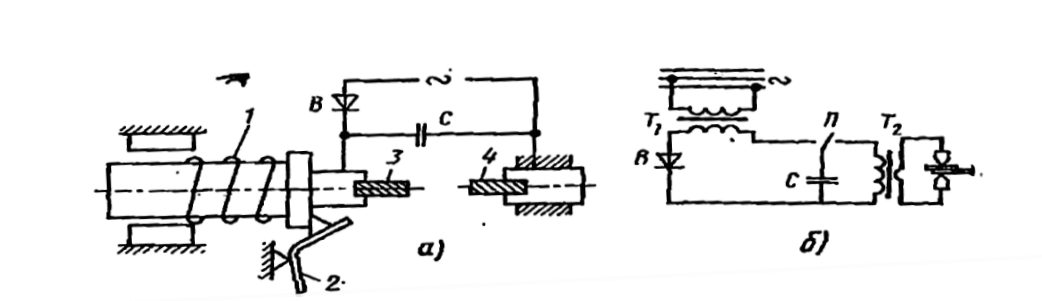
Схемы конденсаторной сварки: а - безтрансформаторная с разрядом на изделие; б - с разрядом на первичную обмотку трансформатора; 1 - пружина; 2 - защелка; 3 -и 4 - заготовки; С -конденсатор; В - выпрямитель; Т – трансформатор
